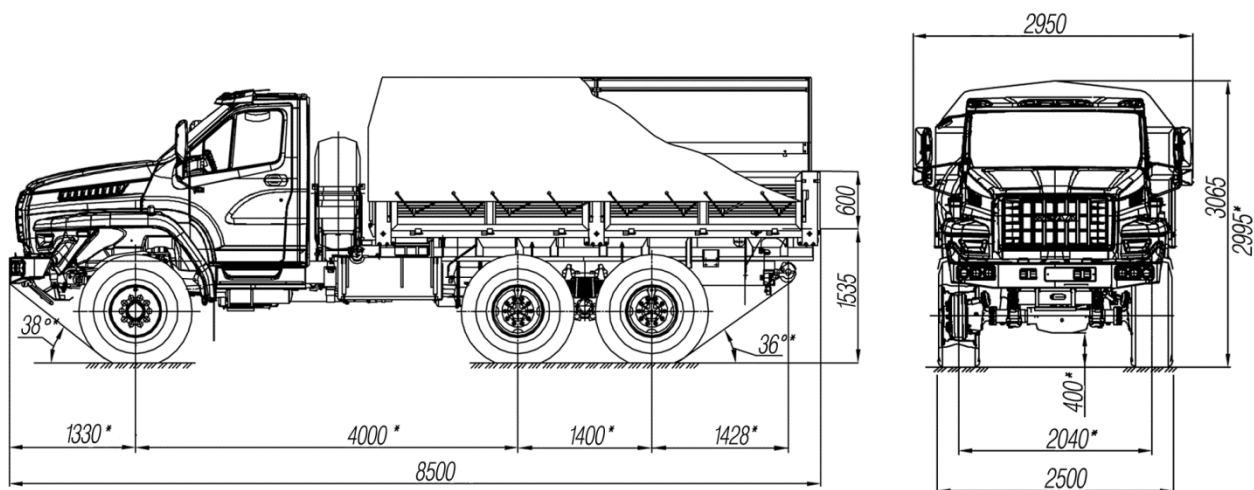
Габаритные размеры автомобиля Урал-4320-5111-73
